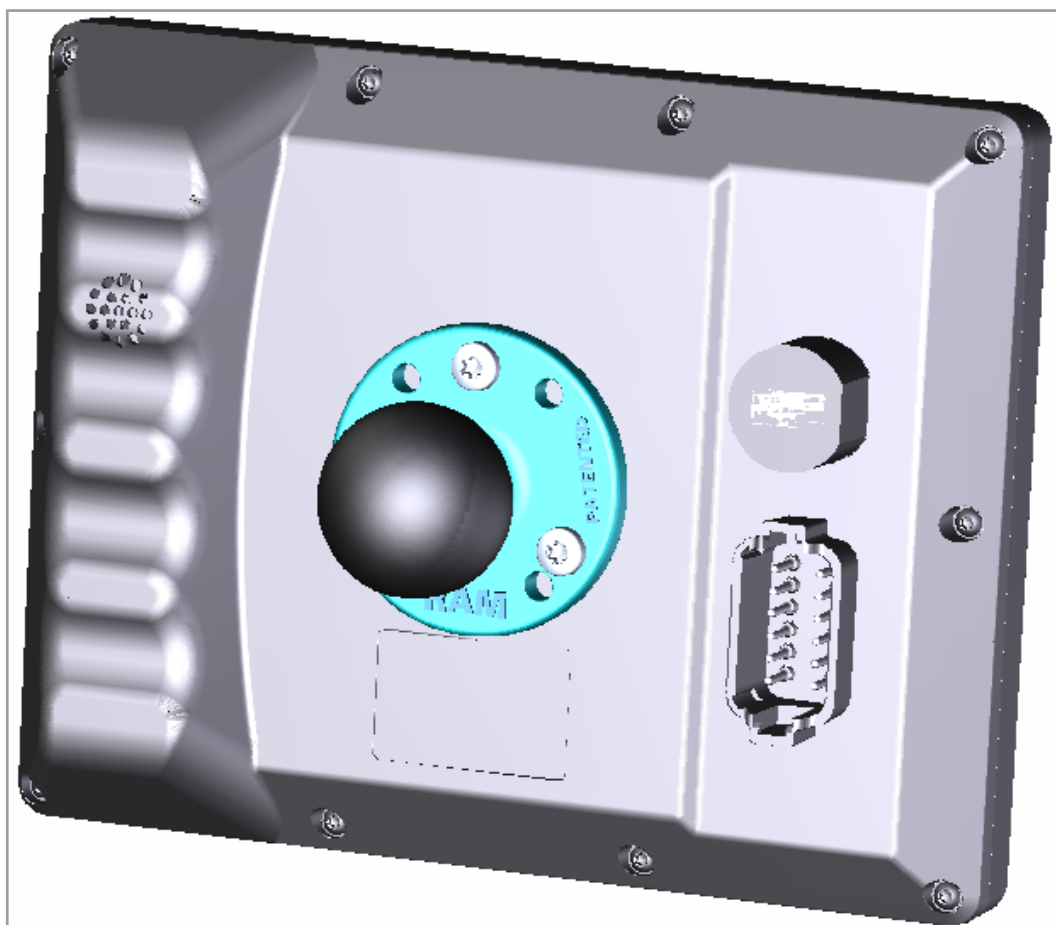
Posizioni di montaggio ammesse con supporto RAM Mount
